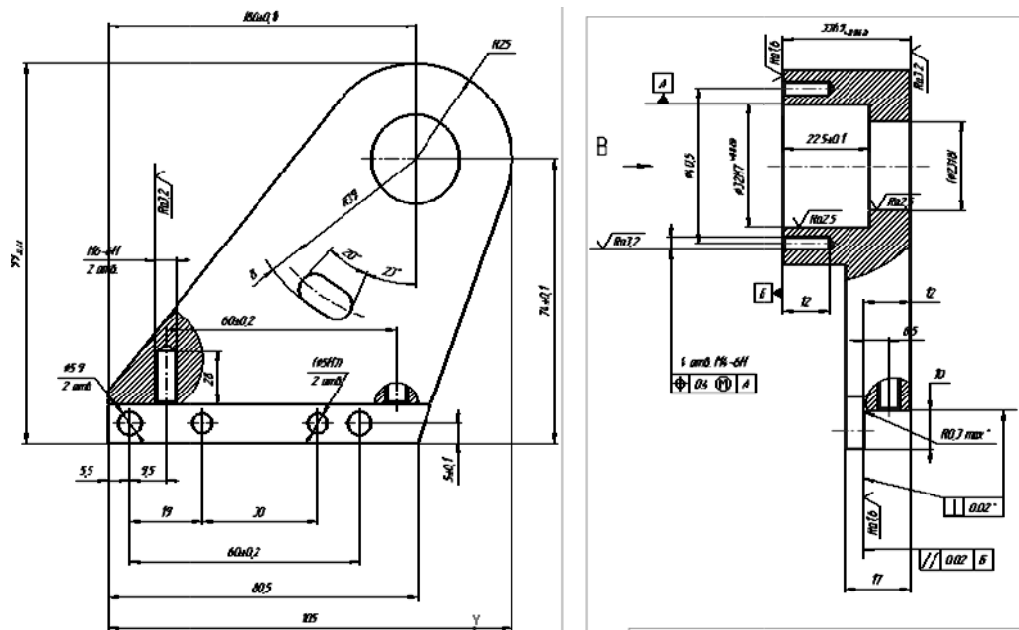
Деталь стійка 247/4/2216-08.01.10
